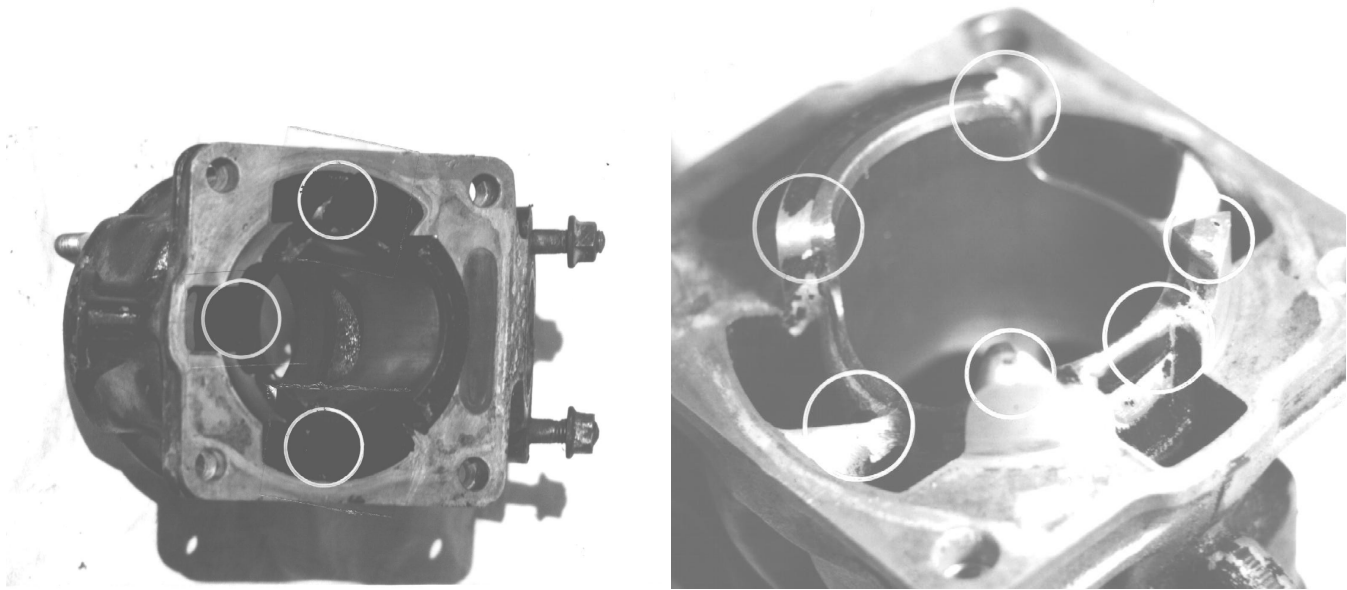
Unterer Zylinder (Einlauf Boost-Port)
